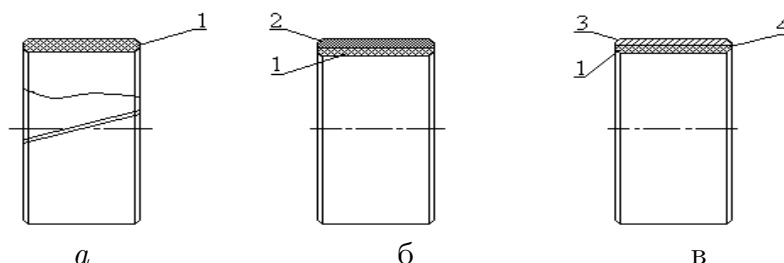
Конструкции СПС на основе ПКМ: а – втулка антифрикционная тонкостенная для гидроцилиндра; б – комбинированный двухслойный полимерный подшипник; в – комбинированный двухслойный металлополимерный подшипник; 1 – МАС-ЗХБН; 2 – упрочняющий слой; 3 – металлическое основание; 4 – клеевой слой
